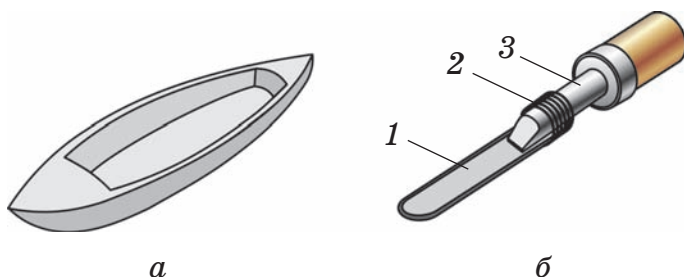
Корпус из пенопласта (а) и терморезак (б):
